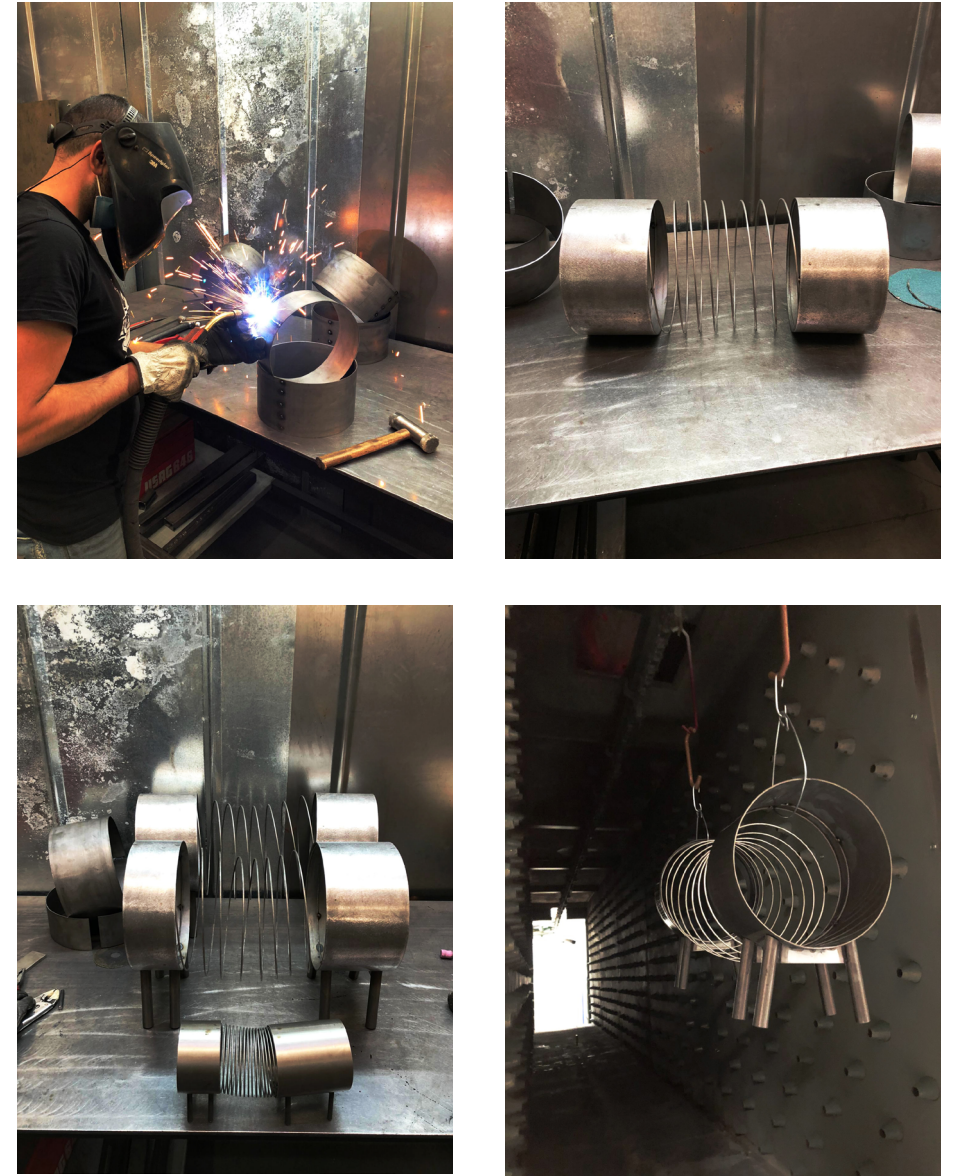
264. 265. 266. Varão, Tubo, Mola e Chapa Calandrada, Corte, Soldadura e Lacagem
